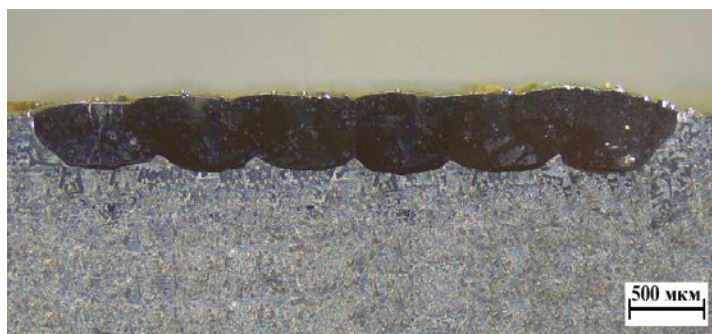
Внешний вид поперечного сечения единичного слоя с шагом наплавки 1,0 мм
